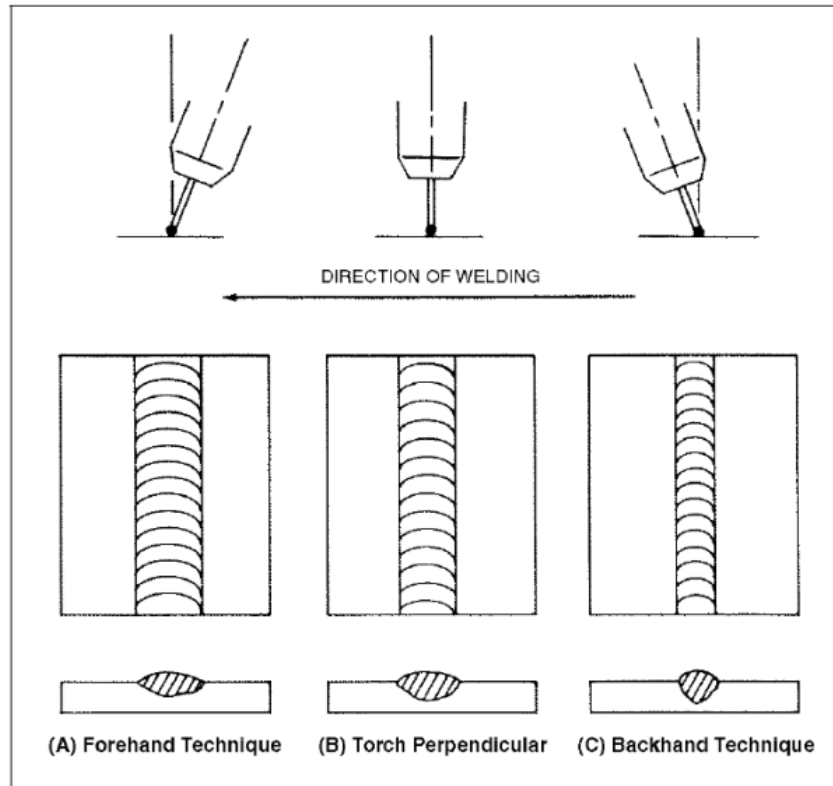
Efeito da orientação da tocha no cordão de soldadura para o sentido empurrando (A), perpendicular (B) e puxando (C) [14].
